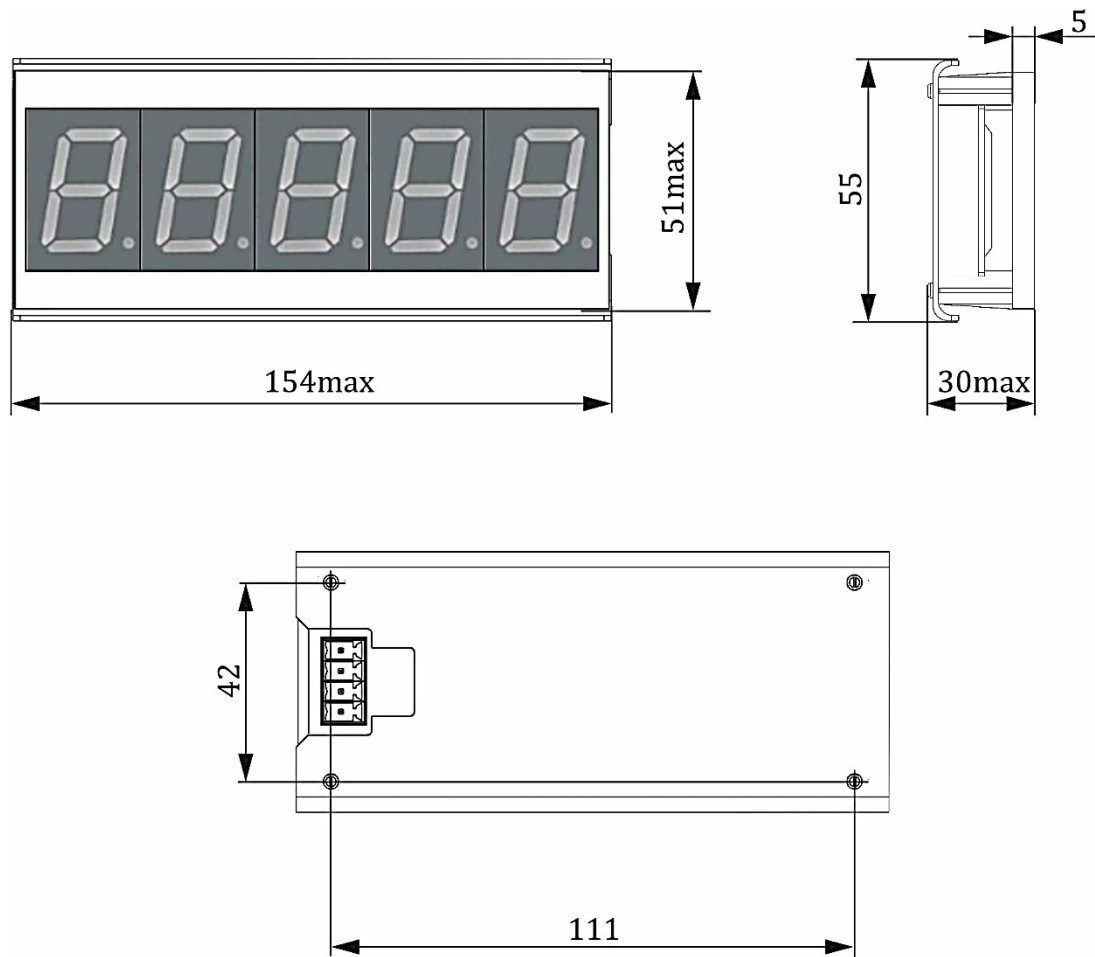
Габаритные и установочные размеры внешнего показывающего устройства E8DU
